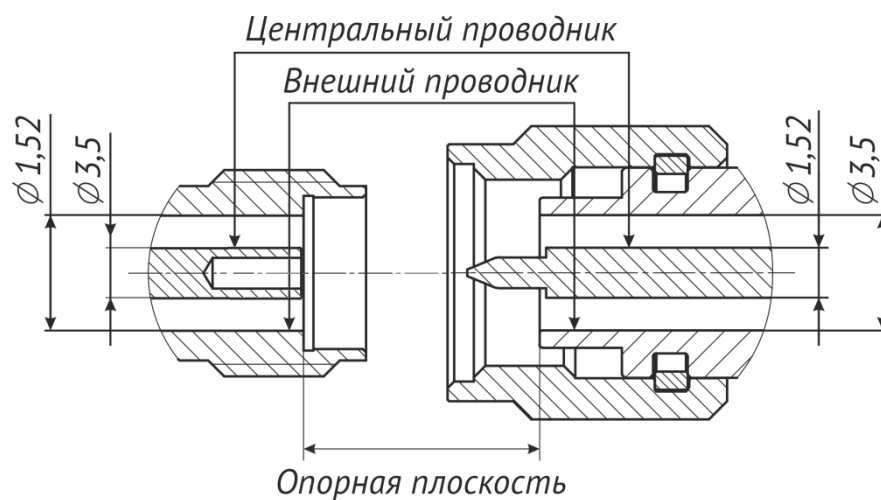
Соединители 3,5 мм и IX, розетка и вилка
